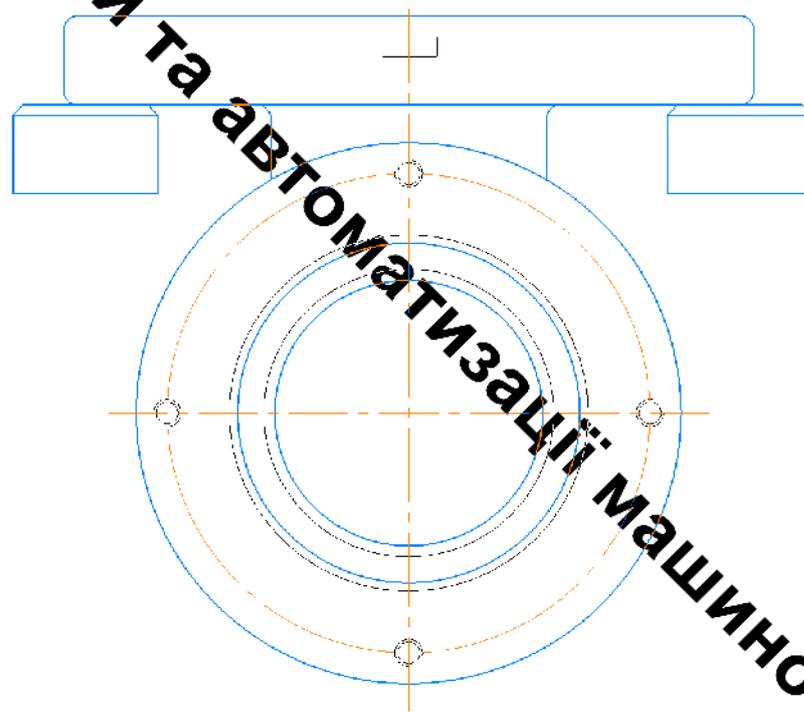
Схема установки заготовки на тактовому столі
